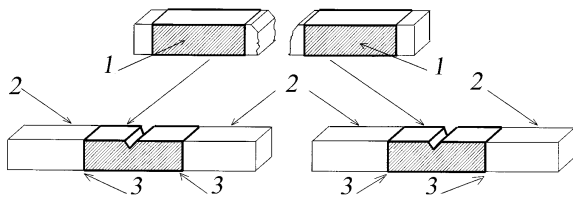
Схема реконструкции образца типа Шарпи: 1 - вставка из половинки испытанного ОС; 2 - хвостовик из необлученной корпусной стали; 3 - сварной шов.
